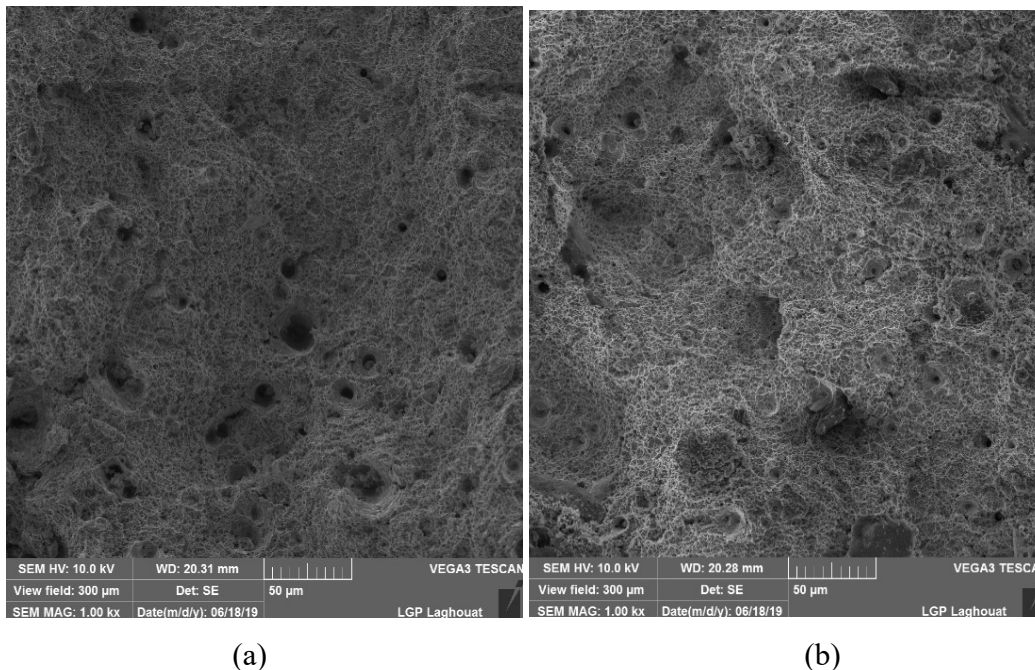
Fractographies des éprouvettes bruts, a) avant et b) après le traitement de vieillissement
